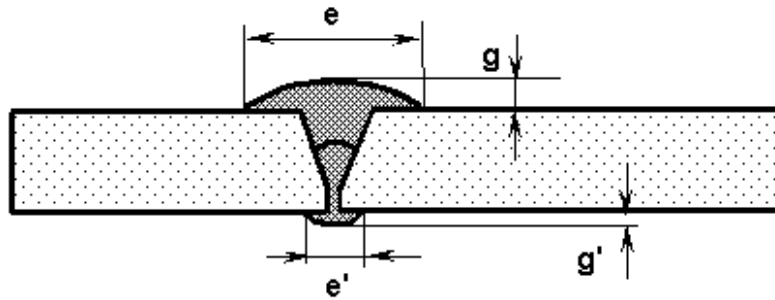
Геометрія стикового з'єднання з обробленням кромки
